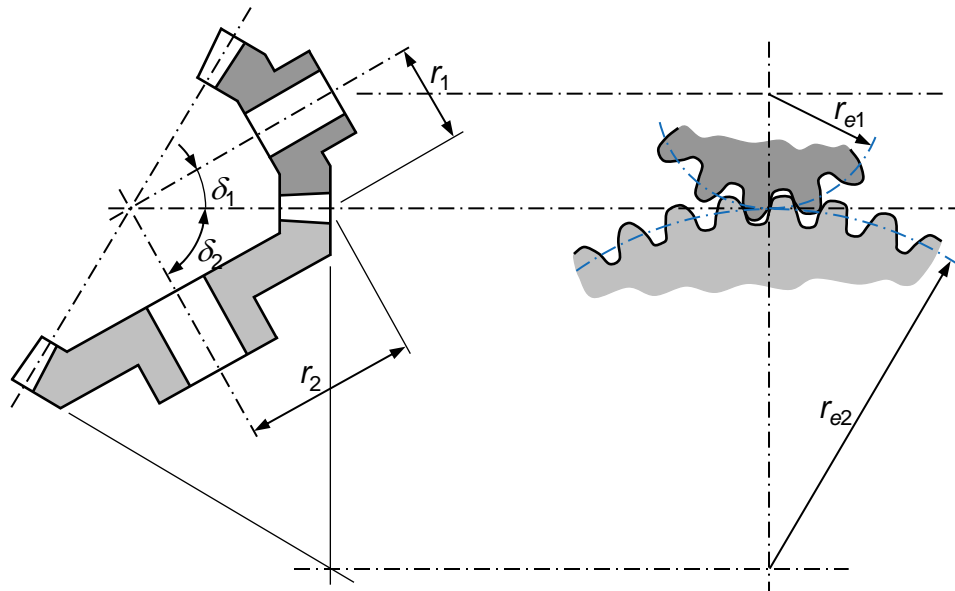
Engrenagem cônica e engrenagem cilíndrica equivalente
